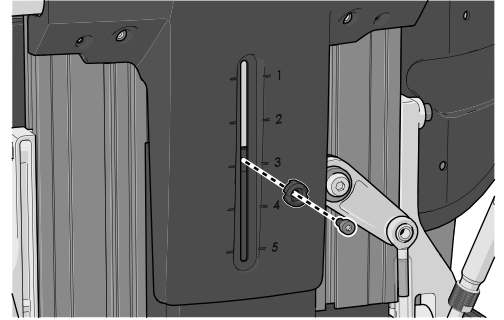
Der Kunststoffknopf ist mit einer Schraube befestigt.
